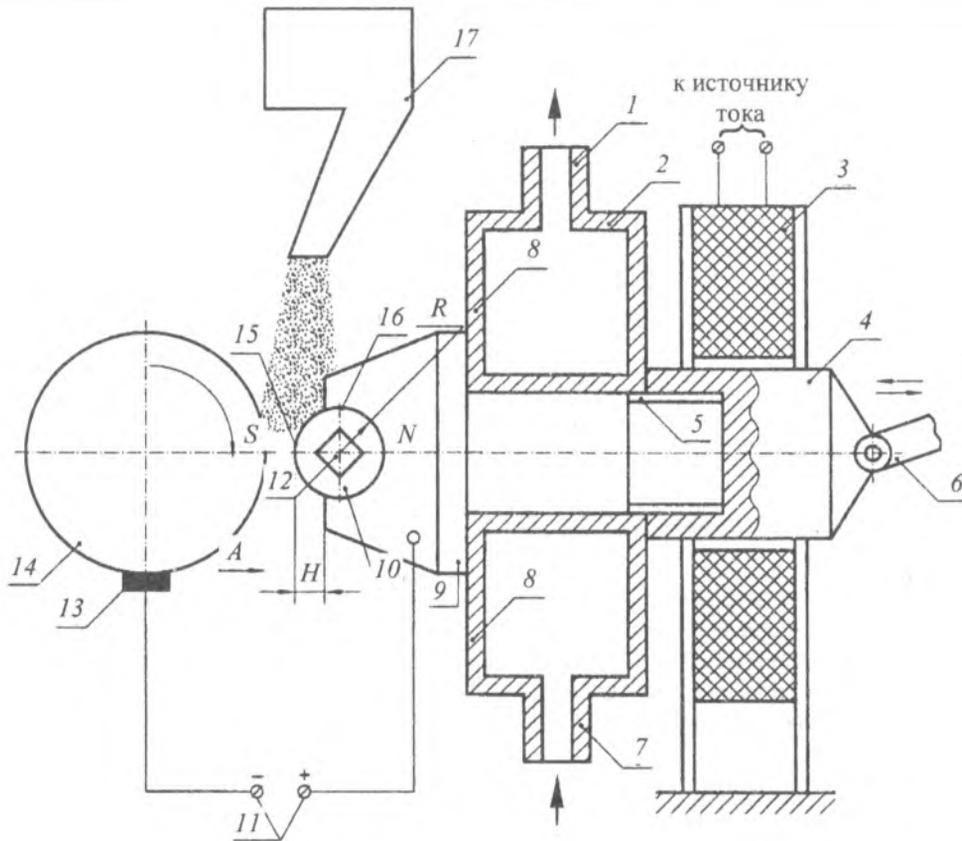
Схема рабочего органа установки для электромагнитной наплавки: 1 – выходной патрубок системы охлаждения; 2 – система охлаждения; 3 – катушка; 4 – сердечник; 5 – резьбовое соединение; 6 – рычаг; 7 – входной патрубок системы охлаждения; 8 – камера; 9 – полюсный наконечник; 10 – цилиндрический ролик; 11 – источник питания; 12 – выступ под ключ; 13 – скользящий контакт; 14 – деталь; 15 – выступ цилиндрического ролика; 16 – гнездо; 17 – бункер
